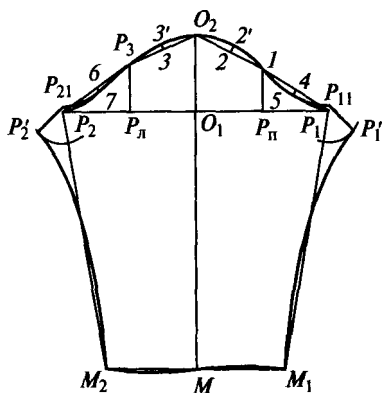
Чертеж конструкции рукава рубашечного покроя для изделия с квадратной проймой
